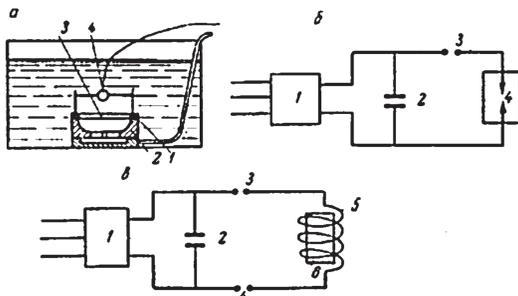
Импульсная штамповка: а) штамповка бризантными веществами: 1 – прижим; 2 – матрица; 3 – заготовка; 4 – подвешенный заряд; б) штамповка с использованием электрогидравлического эффекта: 1 – зарядное устройство; 2 – батарея импульсных конденсаторов; 3 – искровые промежутки; 4 – разрядник, на который подается дозированное количество энергии; в) магнитно-импульсная штамповка: 1 – зарядное устройство; 2 – батарея импульсных конденсаторов; 3, 4 – разрядник; 5 – индуктор; 6 – заготовка
